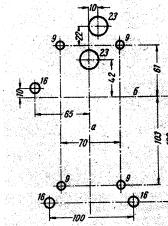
Сверление отверстий для установки на изоляционных пантах контакторов типа КП 503 и КП 513 с задним присоединением
